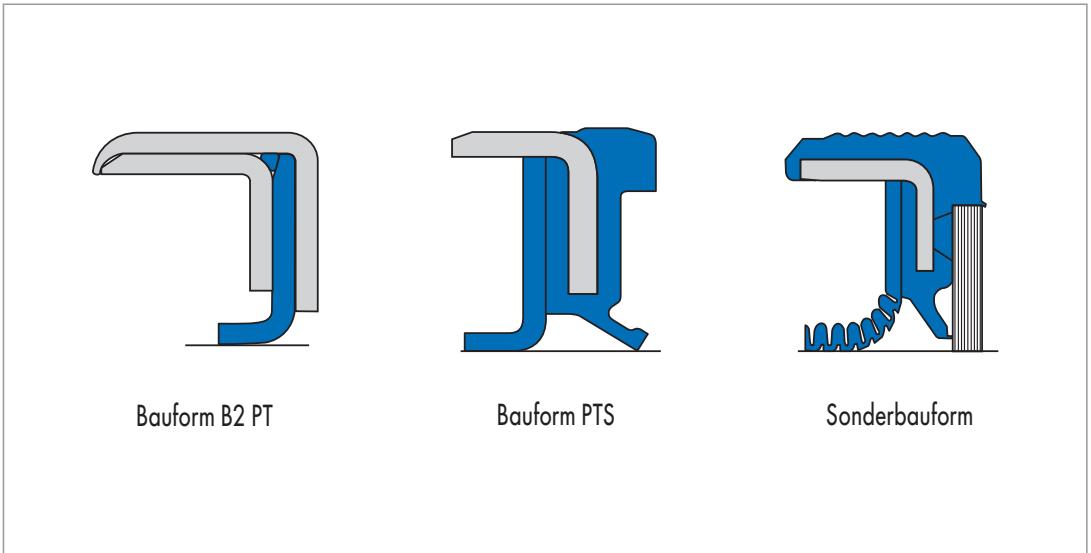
Simmerringe mit Dichtlippe aus PTFE
